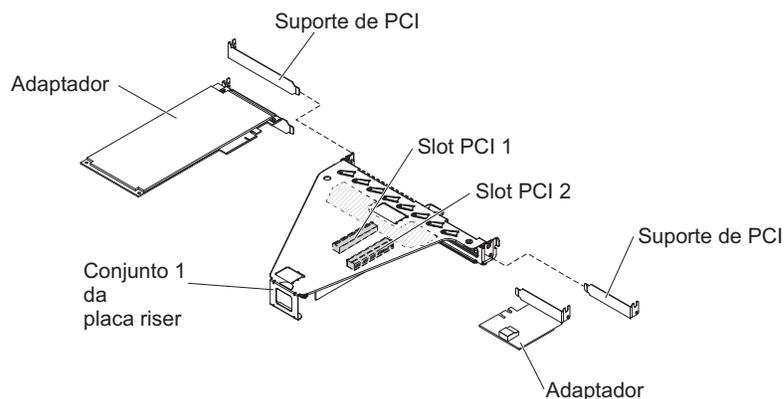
Remoção do Adaptador para o Conjunto da Placa Riser PCI 1
